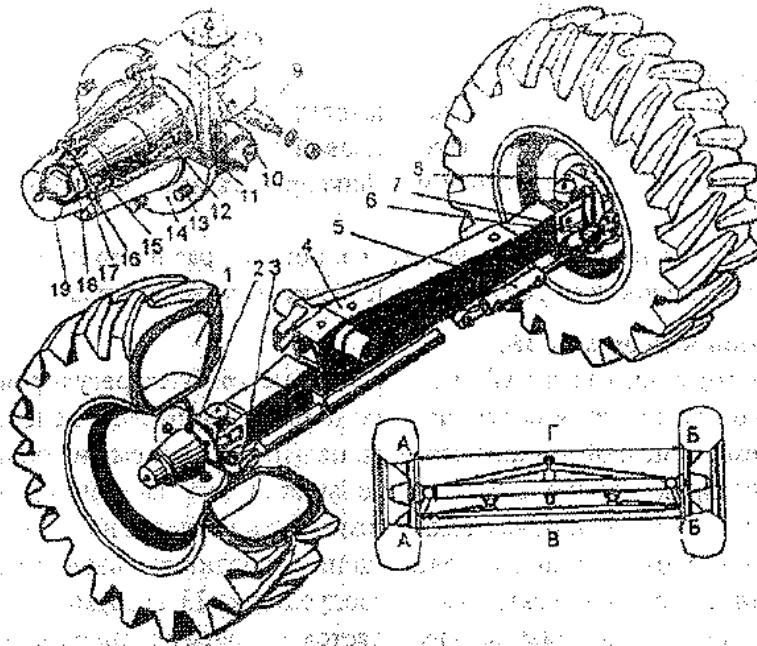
Мост управляемых колес: 1 - колесо управляемое; 2, 8 - кулаки поворотные левый и правый; 3, 7 - рычаги рулевой трапеции; 4 - балка моста; 5 - гидроцилиндры поворота; 6 - тяга рулевая; 9 - клин шкворня; 10 - шкворень; 11 - сальник; 12 - подшипник 7613А; 13 - болты крепления колеса; 14 - ступица; 15 - подшипник 7610А; 16 - втулка; 17 - шайба; 18 - гайка; 19 - колпак ступицы; А, Б - точки замера сходимости колес; В, Г - расстояние между ними
